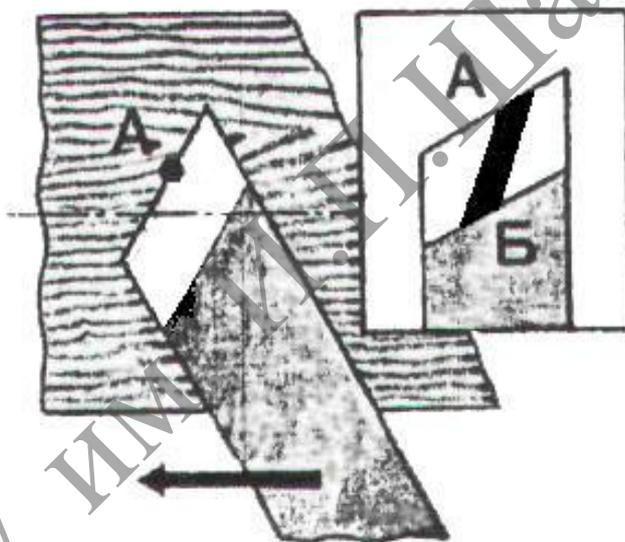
Схема чернового точения полукруглой стамеской
